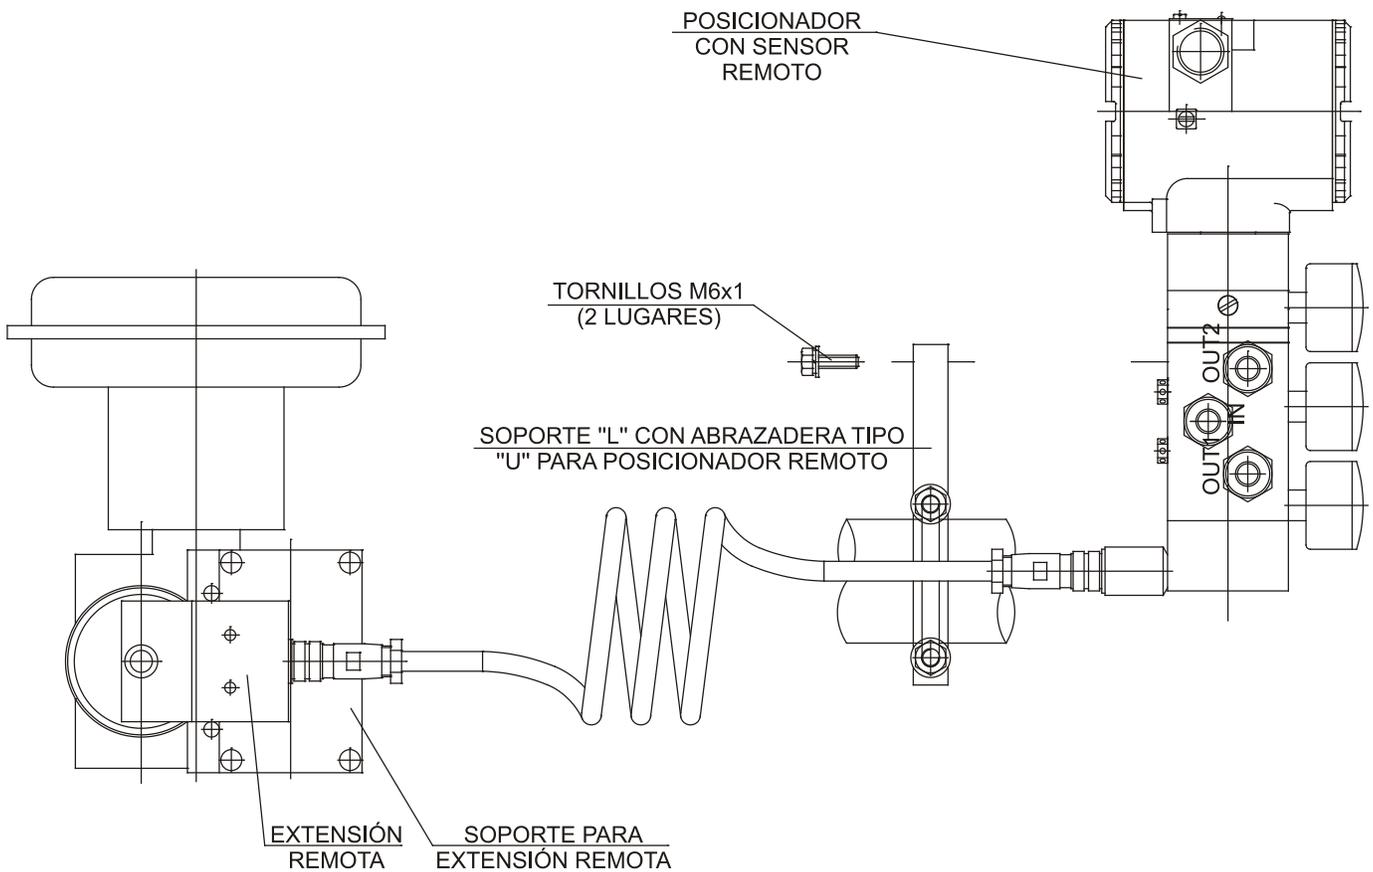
Posicionador en un Actuador Rotativo con Posición Remota
